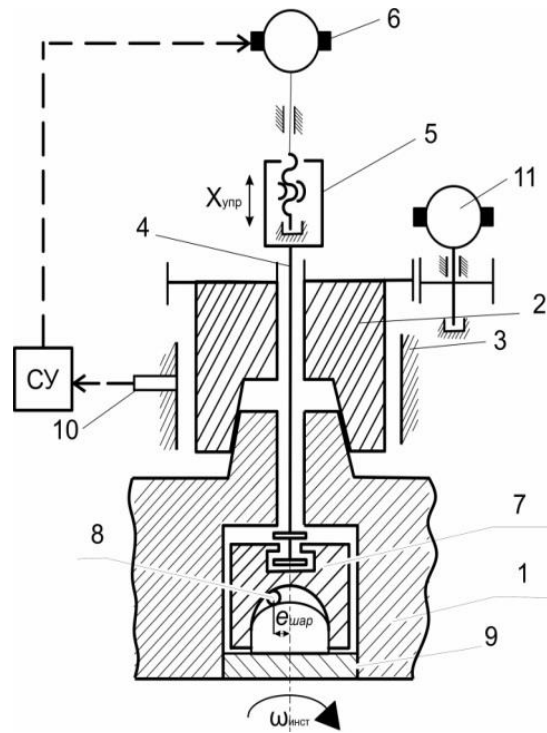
Конструкция шарикового автобалансирующего устройства: 1 – инструмент; 2 – шпиндель; 3 – опора шпинделя; 4 – тяга; 5 – ходовой винт; 6 – двигатель; 7 – подвижный элемент балансира; 8 – шарики; 9 – элемент балансира; 10 – вибродатчик; 11 – привод главного движения; СУ – система управления; « $e_{\text{шар}}$ » – эксцентриситет шарикового балансира; $x_{\text{упр}}$ – управляющее воздействие на подвижный элемент балансира
